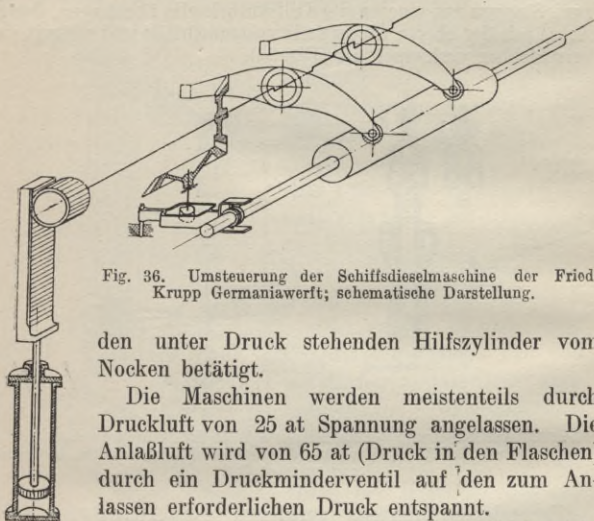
Umsteuerung der Schiffsdieselmachine der Fried. Krupp Germaniawerft; schematische Darstellung.
